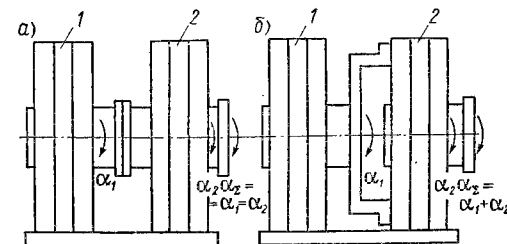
Соединение поворотных гидродвигателей для увеличения вращающего момента (а), для увеличения угла поворота выходного вала (б)
